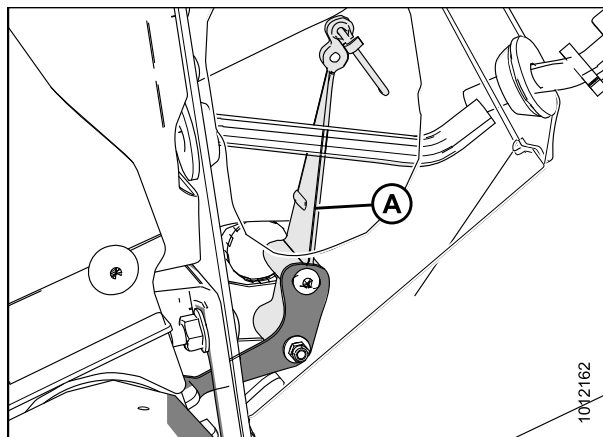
Система регулировки высоты подборщика с правой стороны
